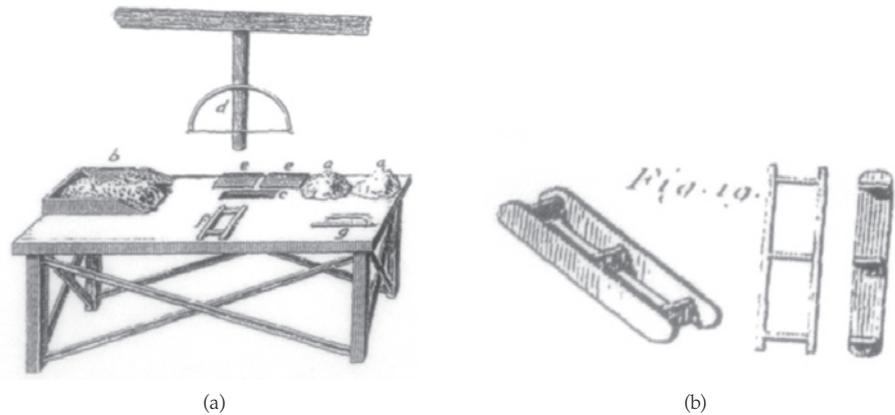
(a) Mesa do moldador; (b) Moldes duplos.
